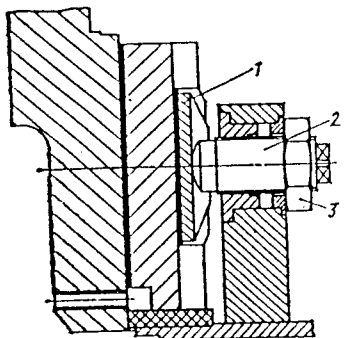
Направляющий подшипник: 1 — сегмент; 2 — опорный болт; 3 — гайка
